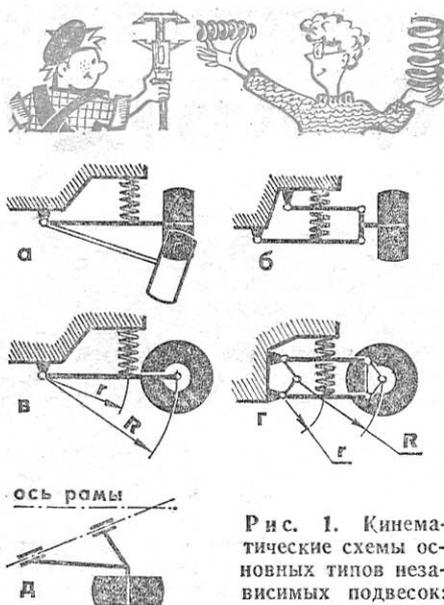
Кинематические схемы основных типов независимых подвесок: а — однорычажная с поперечным рычагом, б — двухрычажная с поперечными рычагами, в — однорычажная с продольным рычагом, г — двухрычажная с продольными рычагами, д — с косым рычагом.
